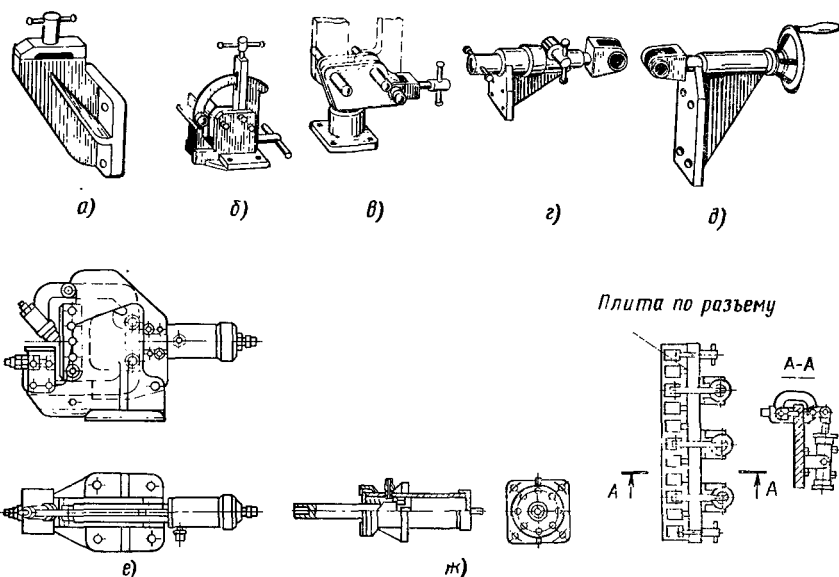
Типовые конструкции фиксирующих и зажимных элементов сборочного приспособления:
